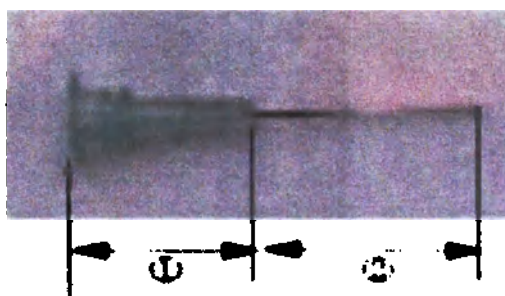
Схема общего вида 1- длина головки, 2- рабочая часть иглы
